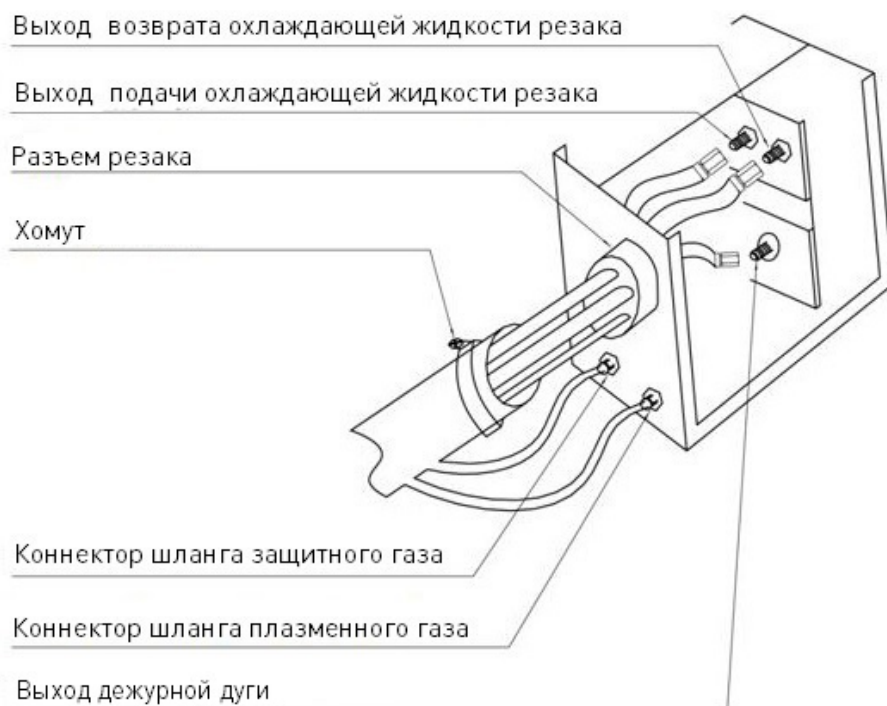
Соединение блока ВЧ поджига и резака.
